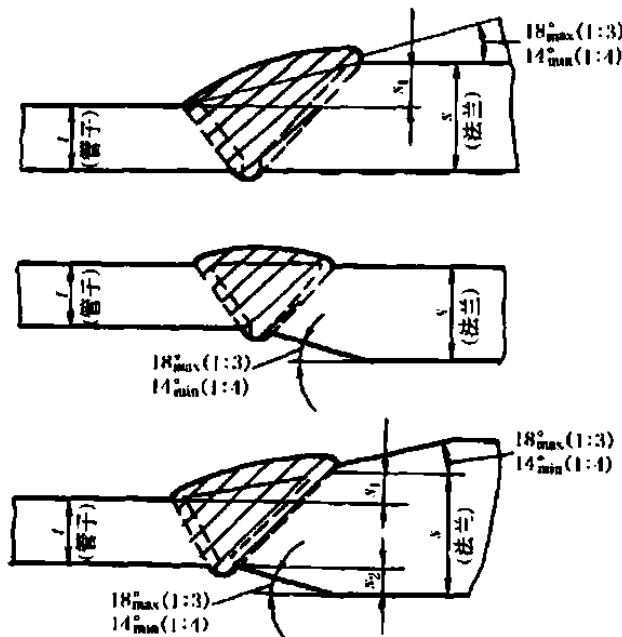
对焊法兰与钢管连接的焊接坡口型式和尺寸
